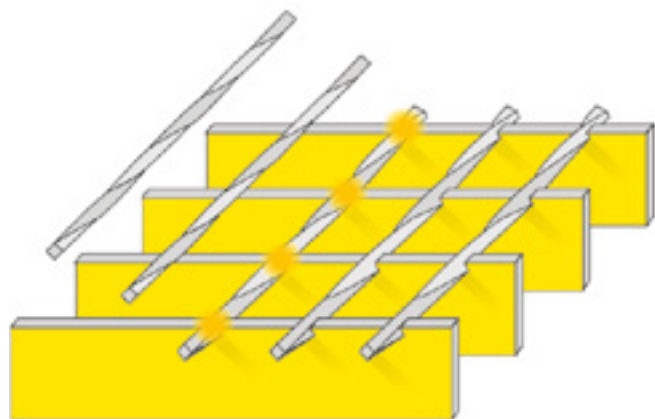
Изготовление сварного решетчатого настила (SP). Поперечные четырехгранные прутки запрессованы в несущие полосы под давлением и одновременно сварены при помощи электросварки.
